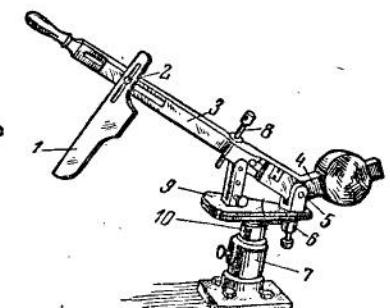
Приспособление с шаблоном для формовки изделий в полых формах
